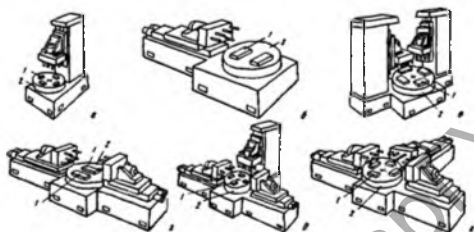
Типовые компоновки агрегатных станков с поворотным делительным столом
